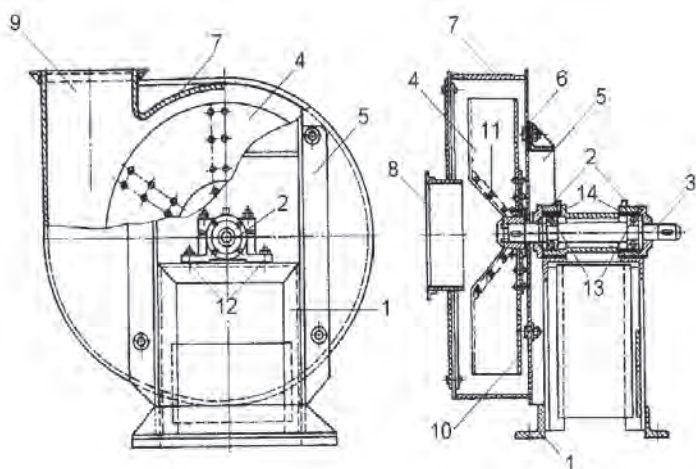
Общий вид малошумного вентилятора; рис.2 – его профильная проекция в разрезе: 1 - рама, 2 - опоры, 3 - вал, 4 - сборное рабочее колесо, 5 - каркас из уголков, 6 - упругие прокладки между корпусом вентилятора 7 и патрубками, 7 - корпус вентилятора, 8 - входной патрубок, 9 - выходной патрубок, 10 - диск, 11 - лопатки рабочего колеса, 12 - упругие прокладки для установки корпуса опор 2 вала 3 на раме 1, 13 - подшипники вала 3, установленные в корпусе опор 2 посредством упругих втулок 14.
